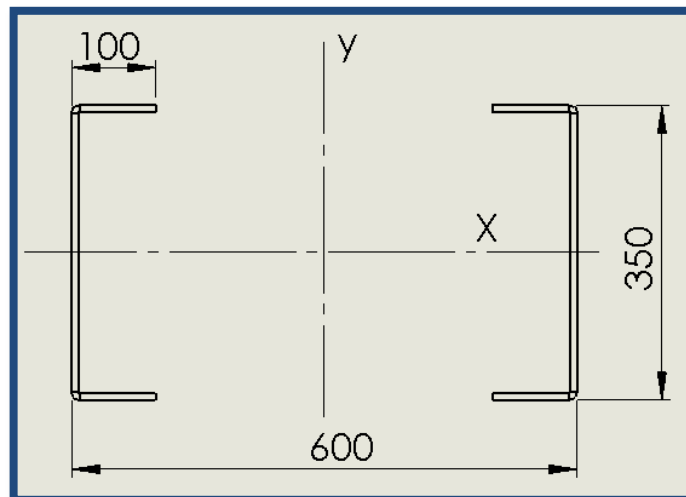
Sección de la viga de la lanza, con medidas generales.
